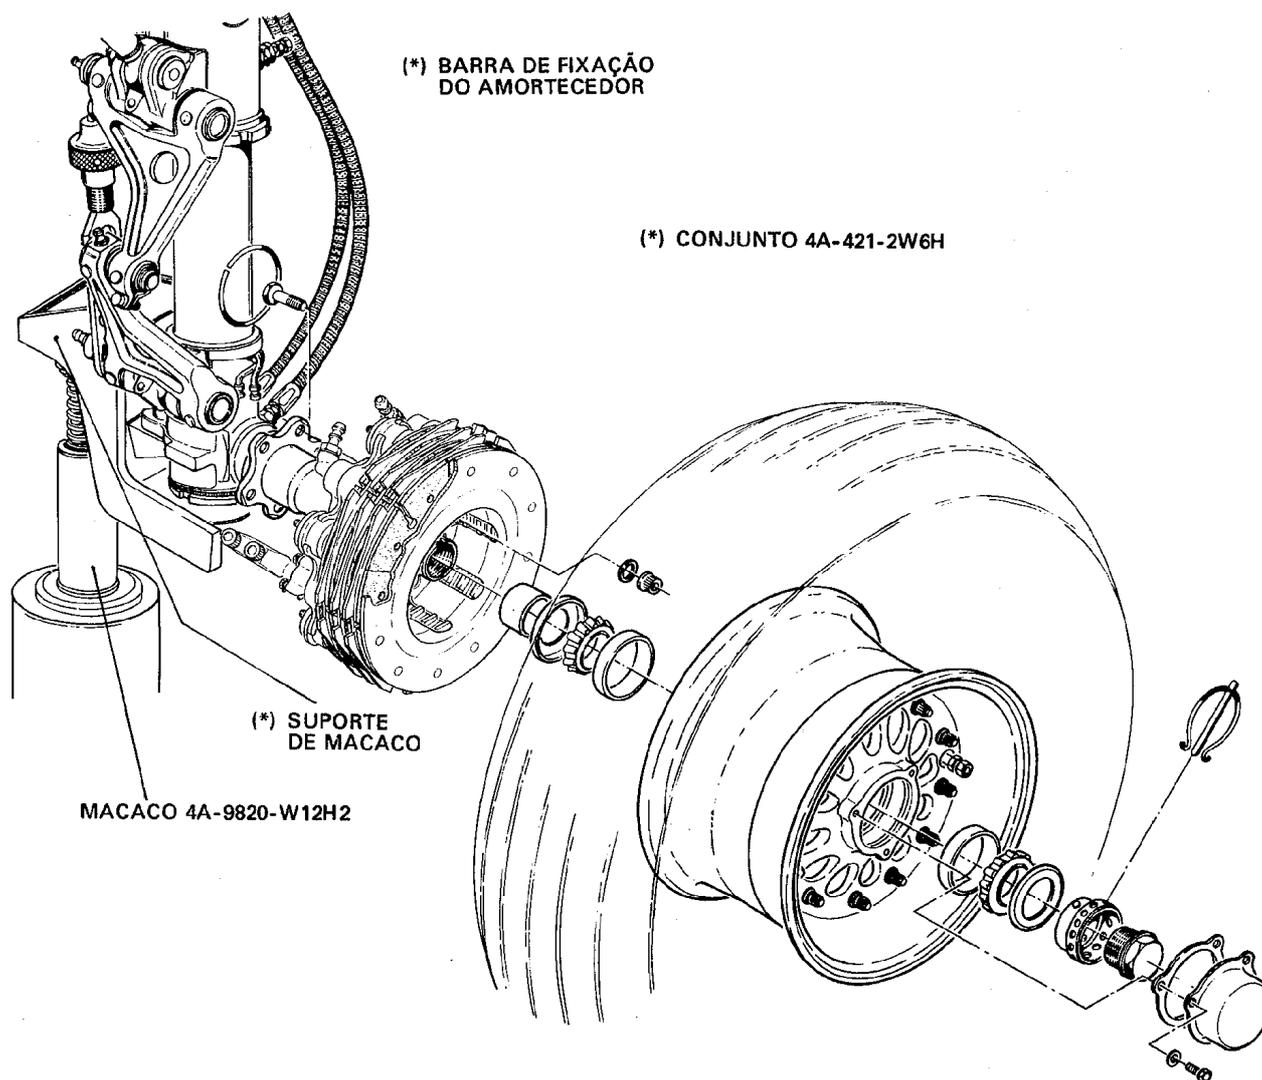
Instalação do Conjunto da Roda do Trem de Pouso Principal (ERAM)
